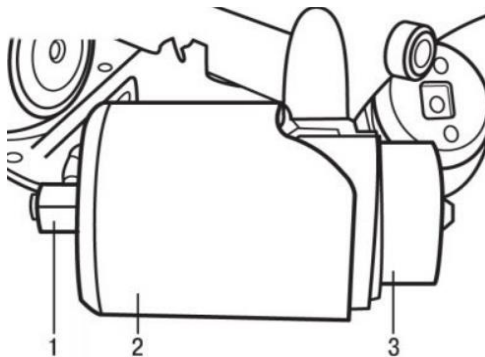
Положення пристроїв на опорному кронштейні балки задньої підвіски для випресування шарніра: 1 - болт тяги 0543-С; 2 - конус для випресування 0543-Е; 3 - напрямний елемент/опора 0543-В
